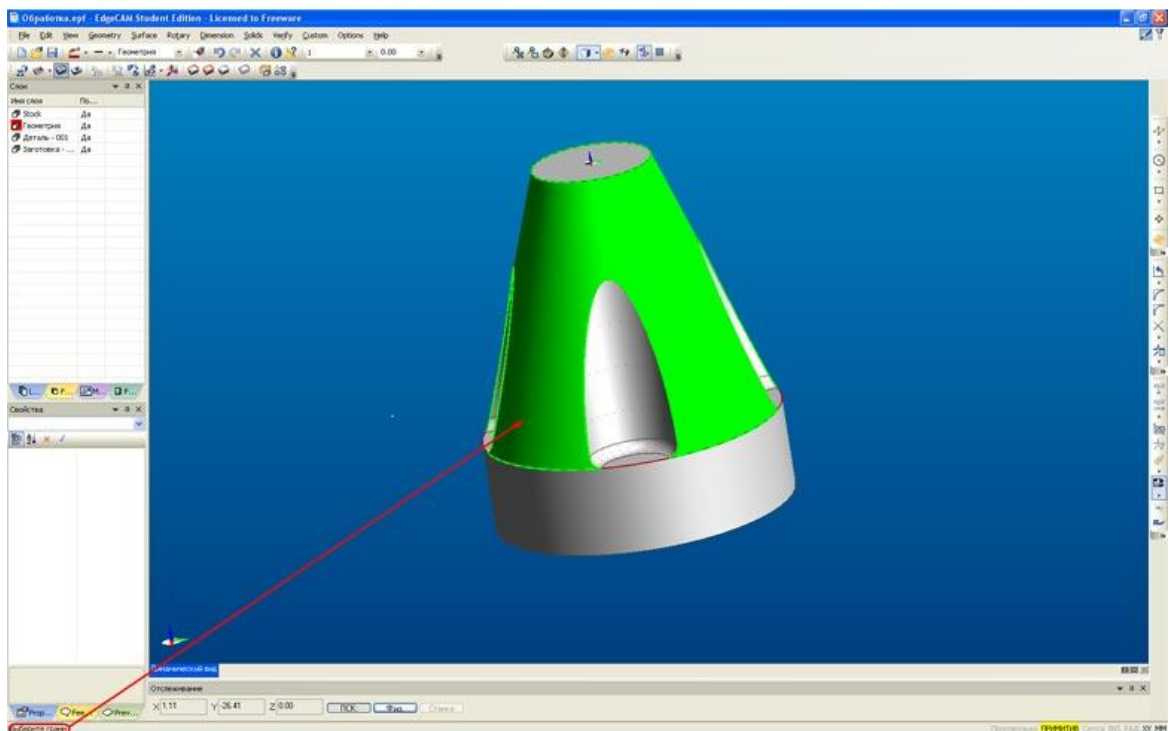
Edgescam. Выбрать обрабатываемые поверхности
